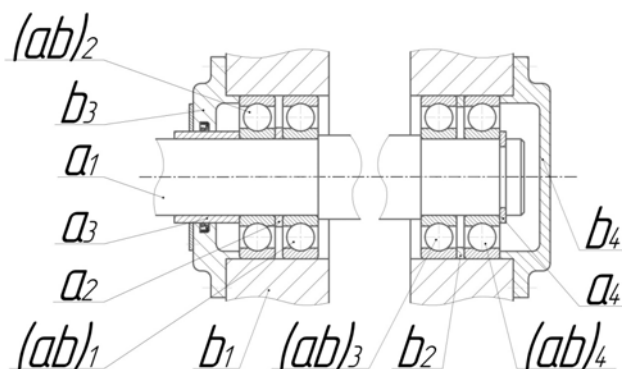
Вал с 4-мя подшипниками в корпусе обозначенный
